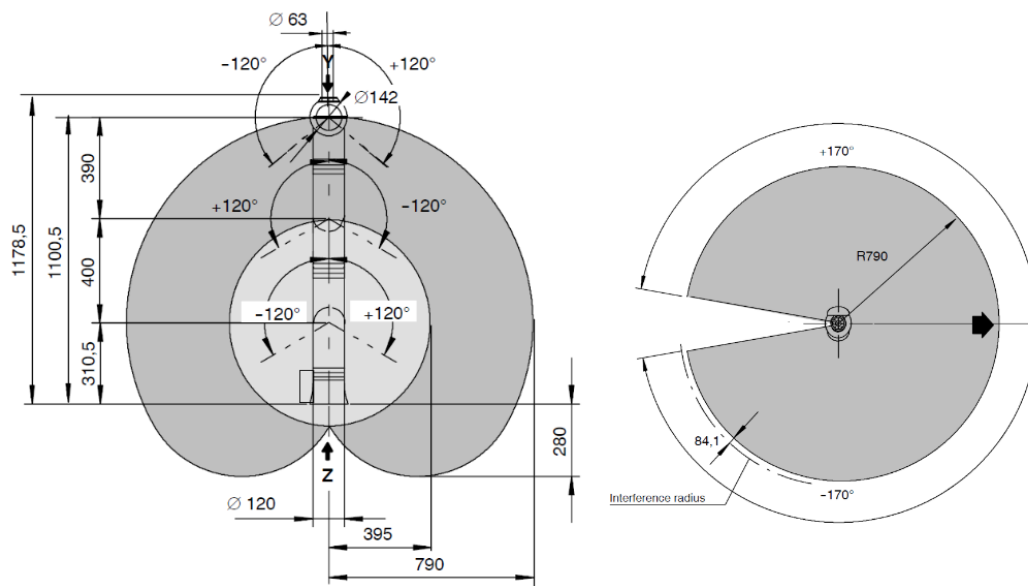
Abgebildet ist der Arbeitsraum des LWR. Auf der linken Seite ist die Seitenansicht und auf der rechten Seite die Draufsicht illustriert. Die Maße sind in mm angegeben. Abbildung entnommen aus [Pedersen \[2000\]](#).
